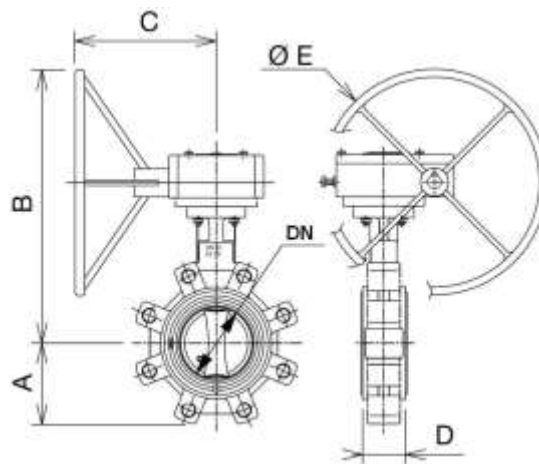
Габаритные и присоединительные размеры затворов дисковых поворотных модификации VFY-LG с отверстиями под болты
